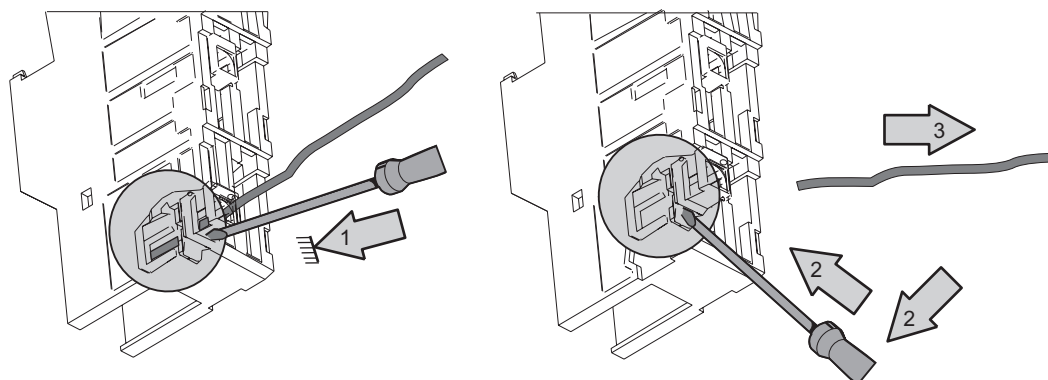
Défaire le câblage d'un module terminal avec Fast Connect
